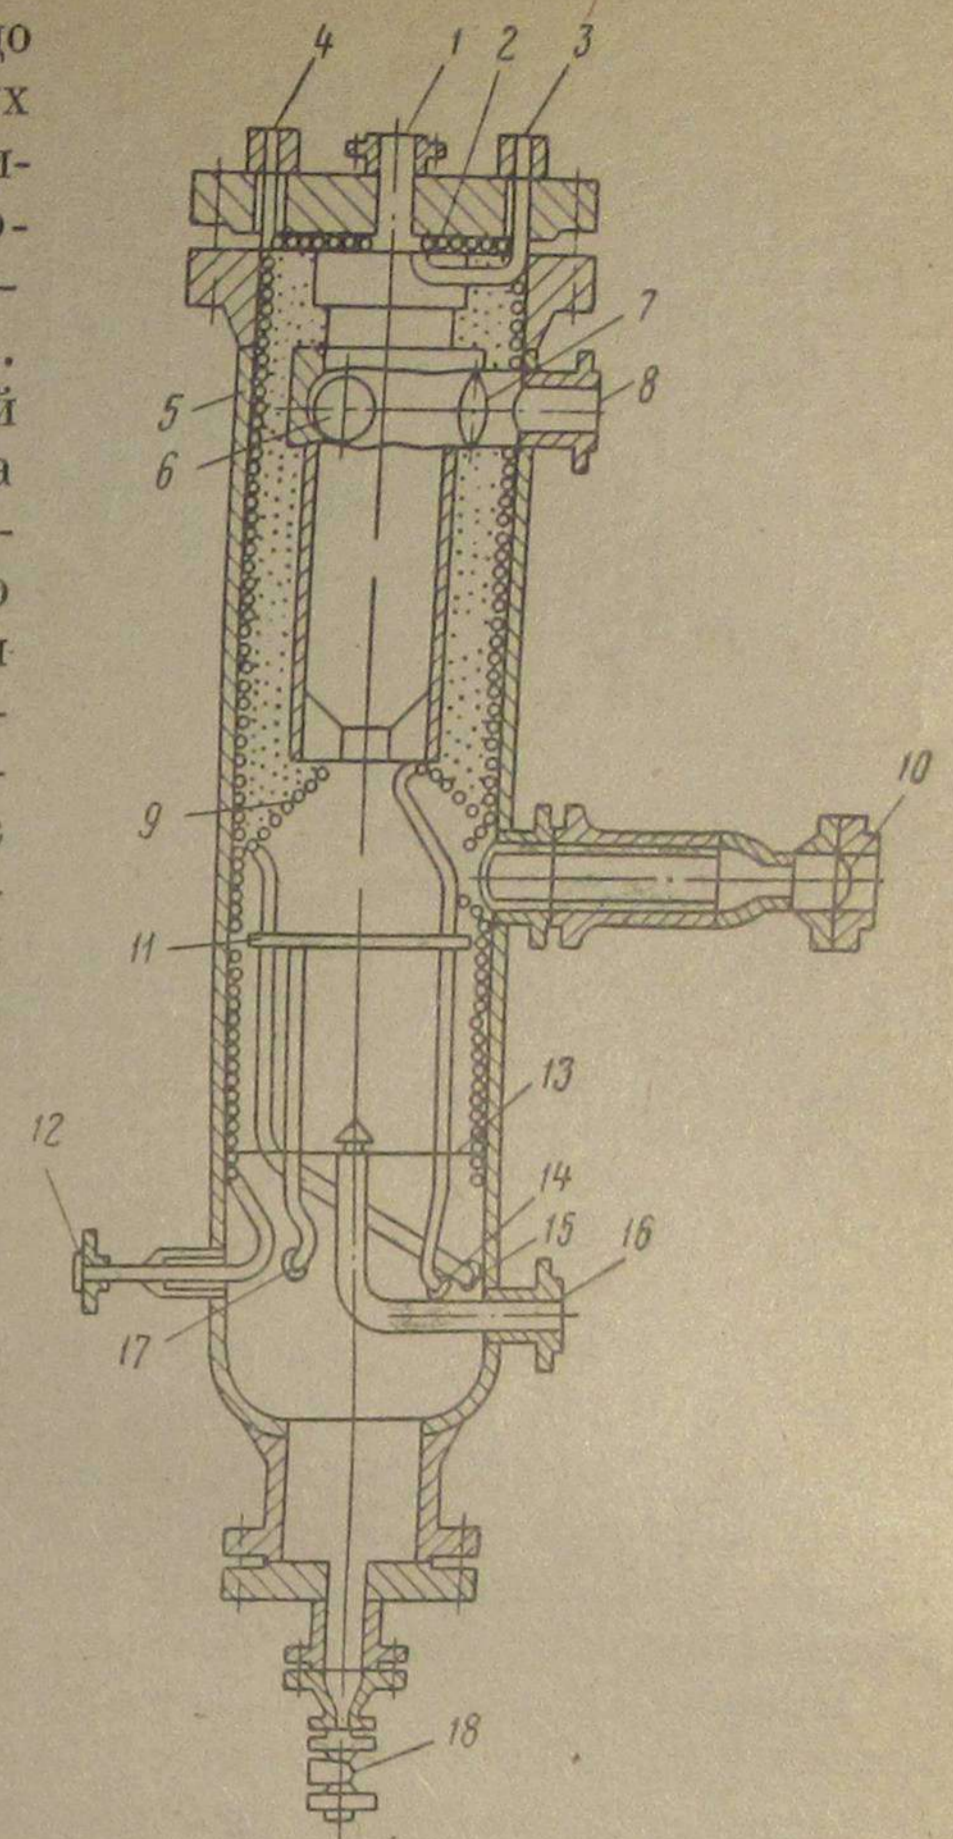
Газогенератор системы Горного бюро США для газификации пылевидного топлива под давлением:
